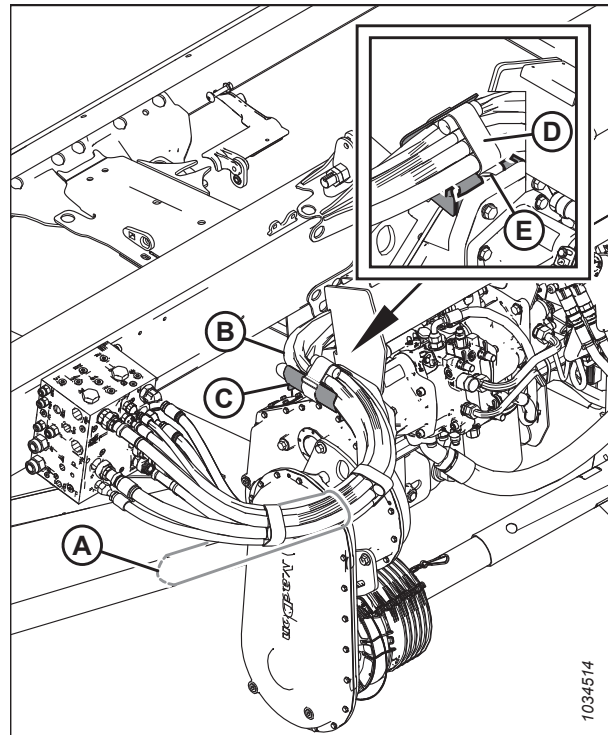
Flexibles hydrauliques – Configuration étroite
